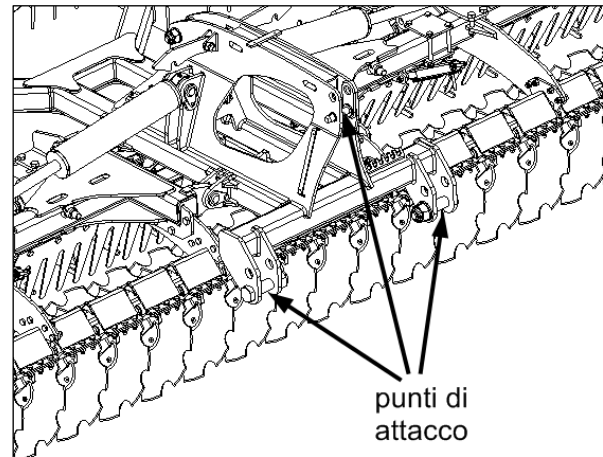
Punti aggancio al trattore (macchina portata) / Tractor connection points (mounted machine)
